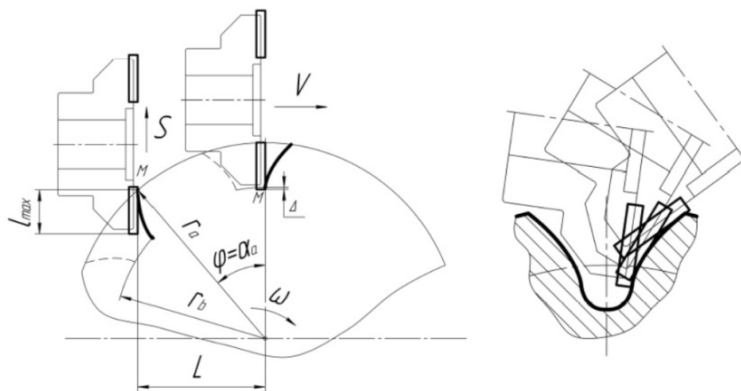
Схема обработки зубчатого колеса методом непрерывного обката [1]
